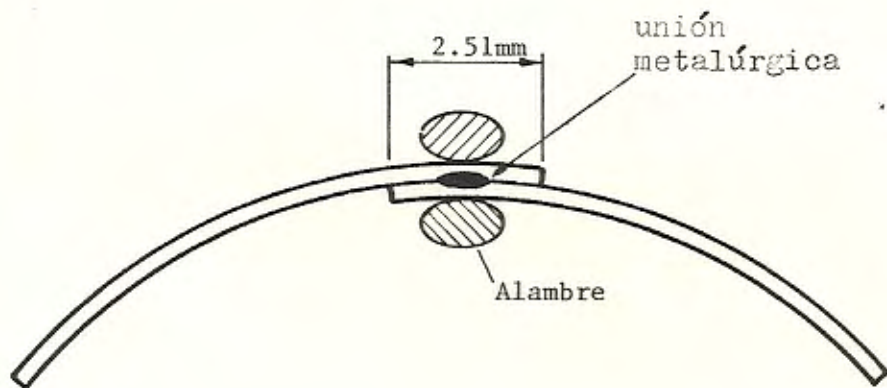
Ancho de solapa de soldadura Soudronic semi-automática.
